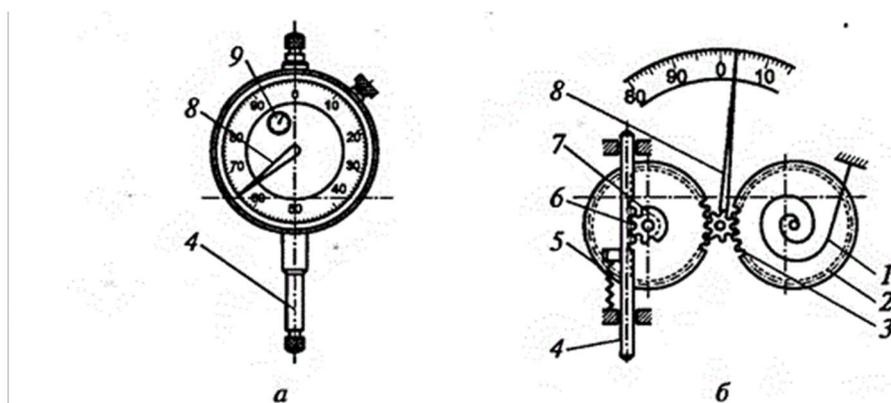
Индикатор часового типа(а) и его схема (б). 1 – спиральная пружина; 2,3,5 и 7 – зубчатое колесо; 4 – стержень; 6 – зубчатая рейка; 8 и 9 – стрелка
